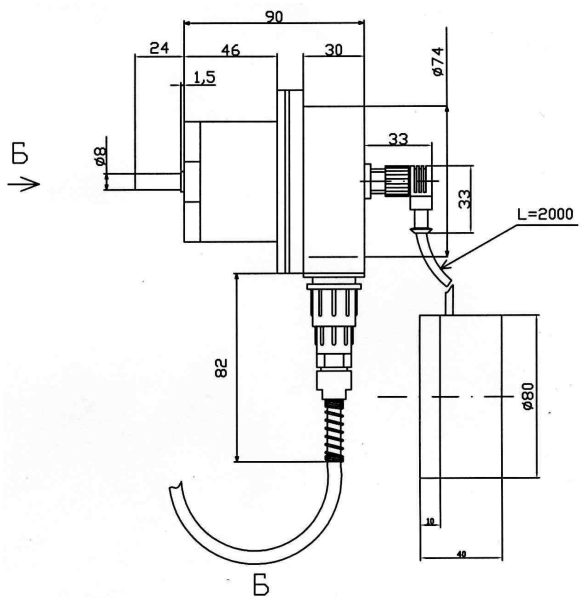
Габаритные и присоединительные размеры датчика ДПИ
